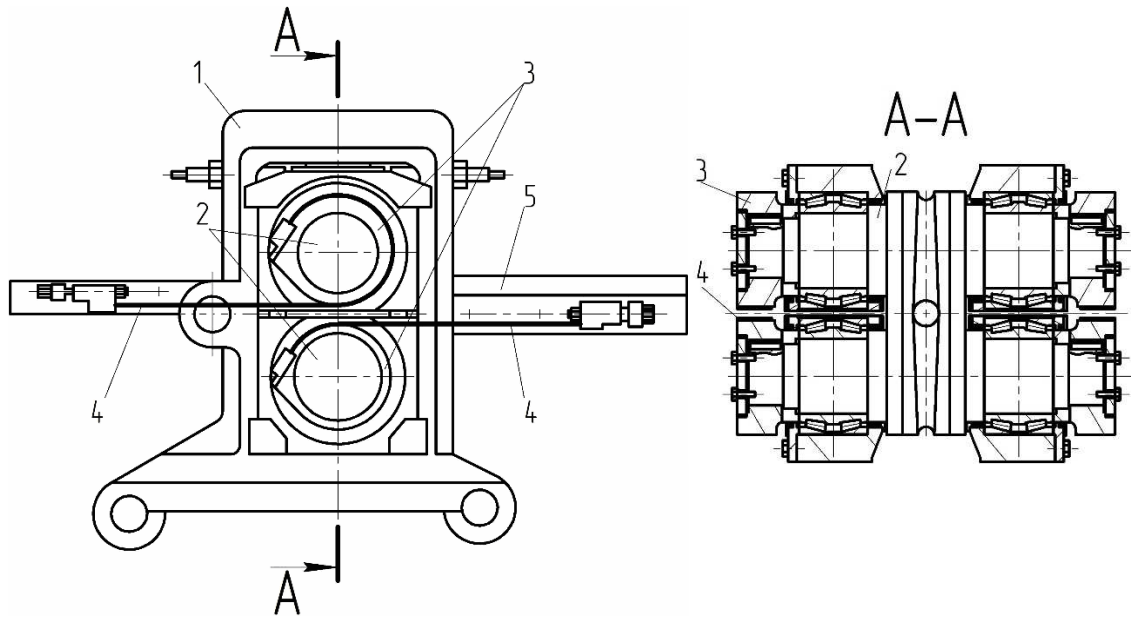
Привод прокатных валков с гибкой упругой связью: 1 – корпус; 2 – прокатные валки; 3 – ведущий шкив; 4 – упругая связь (стальная лента); 5 – станина
